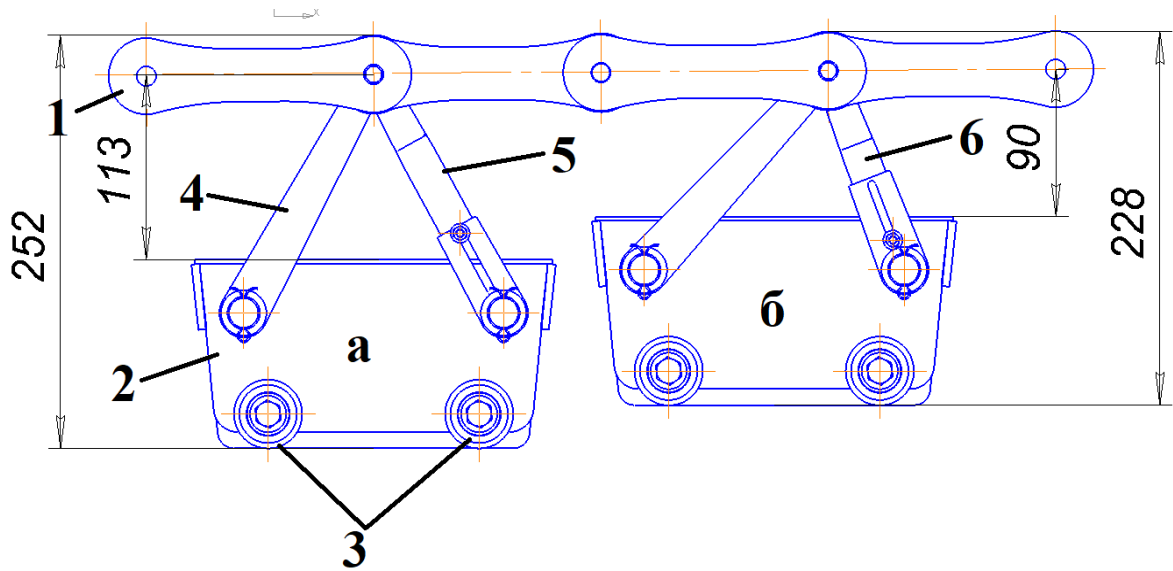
Будова люльок вистійно-пічного агрегату: а – люлька в розкладеному вигляді; б – люлька в складеному вигляді; 1 – ланцюг; 2 – пластина для утримання форм та тяг люлькового механізму; 3 – ролики для руху люльок по направляючим; 4 – нескладна тяга; 5 – складна тяга (Розкладене положення); 6 – складна тяга (Складене положення).
